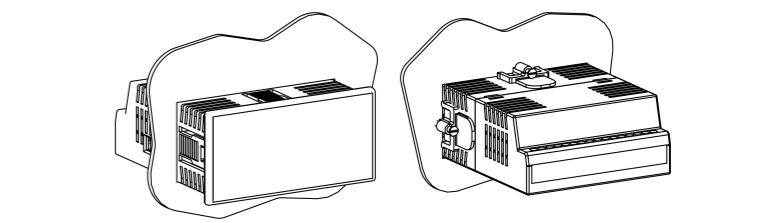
Монтаж прибора щитового крепления Щ2
